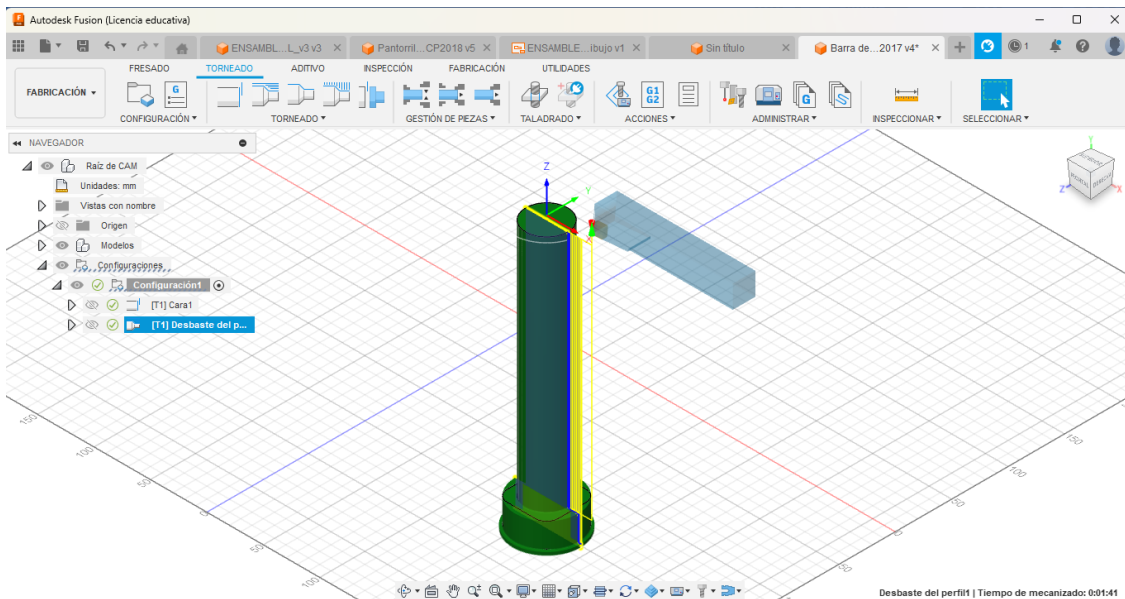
Maquinado de la pieza Interfaz /conexión Rodilla ICR2017
